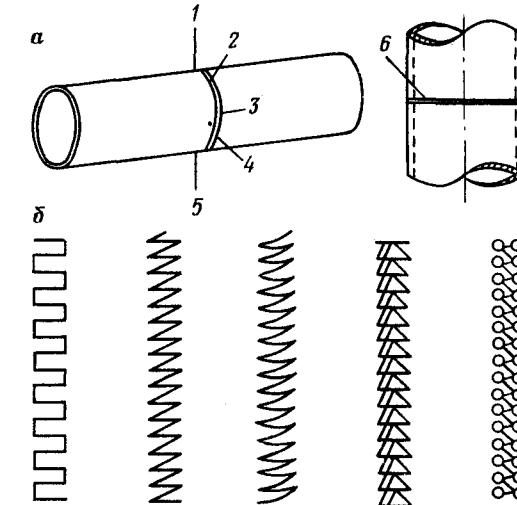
Схема положения электрода (а) при сварке трубопроводов:
